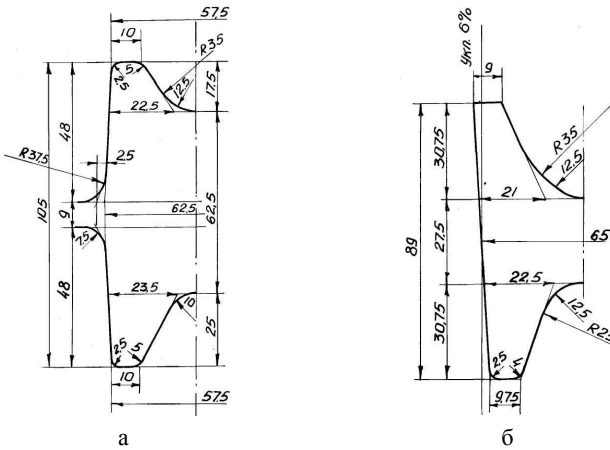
Расчетная схема разрезного калибра – а и следующего за ним калибра – б
